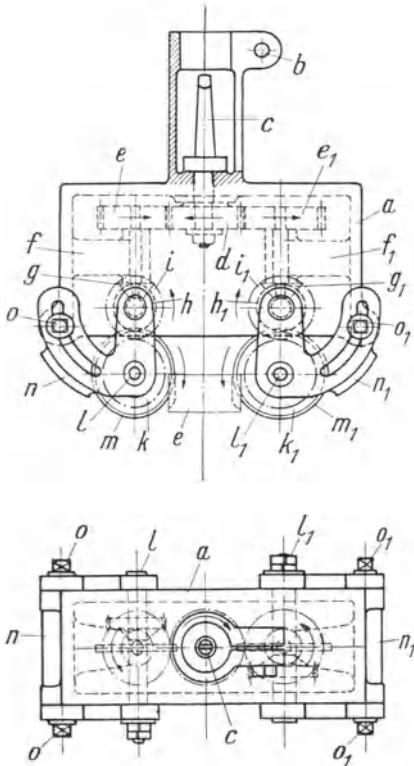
Fräsvorrichtung zum Fräsen der Spannschlitz für Abb. 545.
